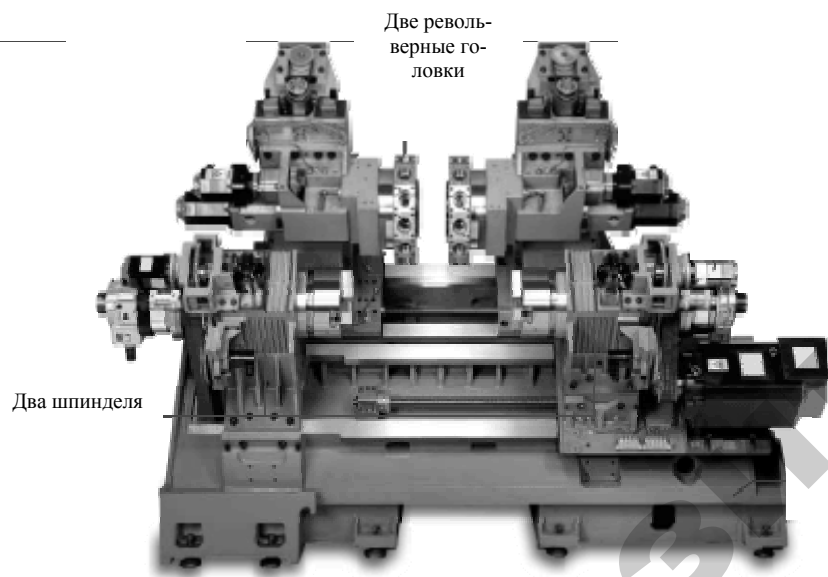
Двухшпindelный двухревольверный токарный обрабатывающий центр
